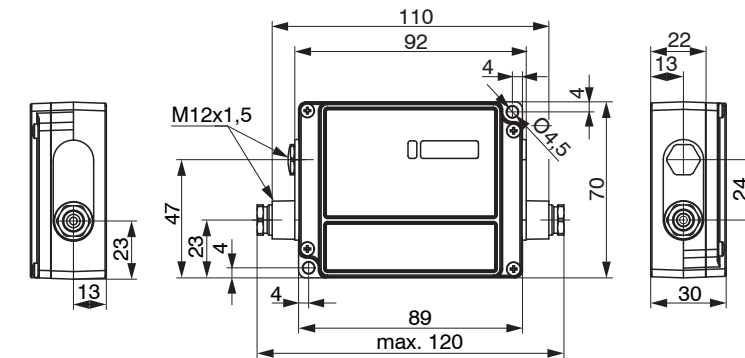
Maßzeichnung Controller, Abmessungen in mm, nicht maßstabsgetreu
